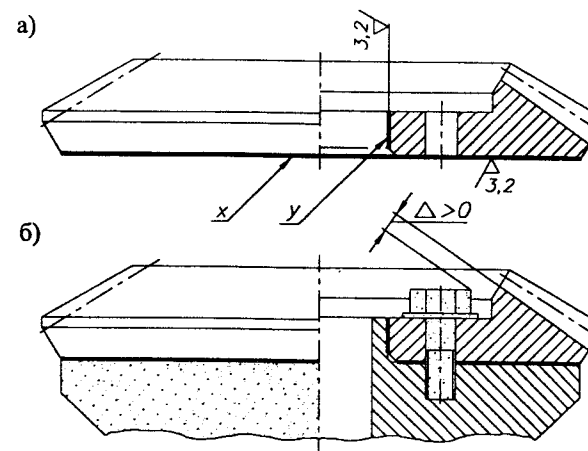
Установочные базы для нарезания зубьев на колесах-дисках
